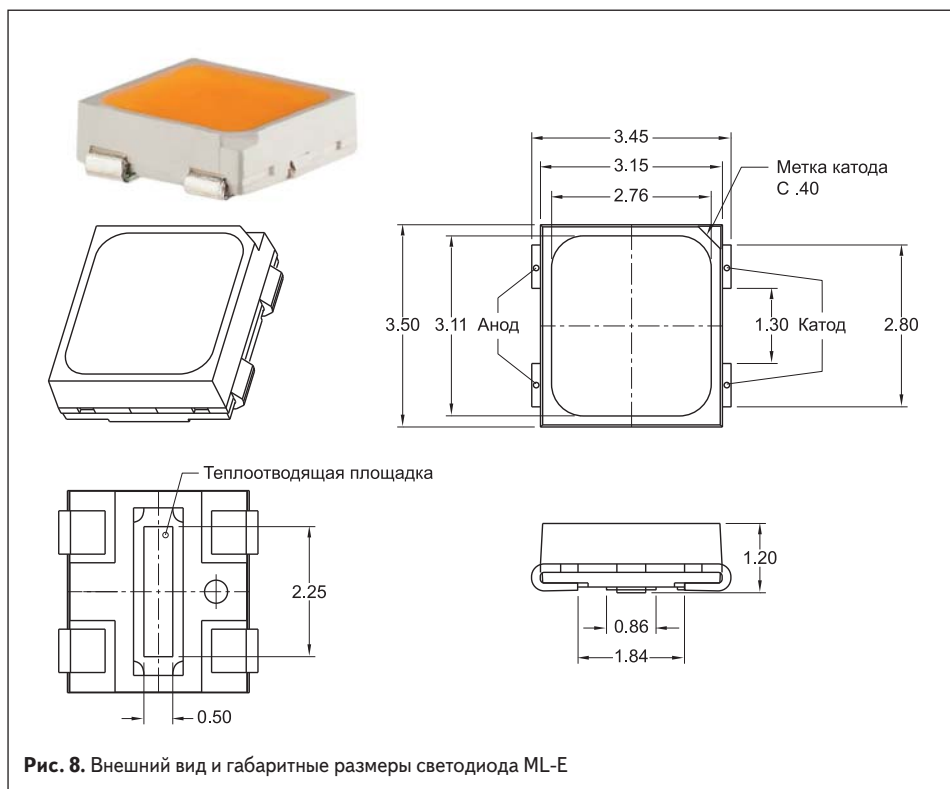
Внешний вид и габаритные размеры светодиода ML-E
